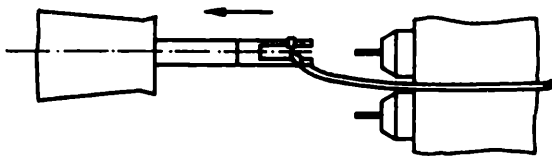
Arbeitsablauf beim Kontaktieren des Leiters und Abschneiden des Drahtes des mit SKT-Handwerkzeug
